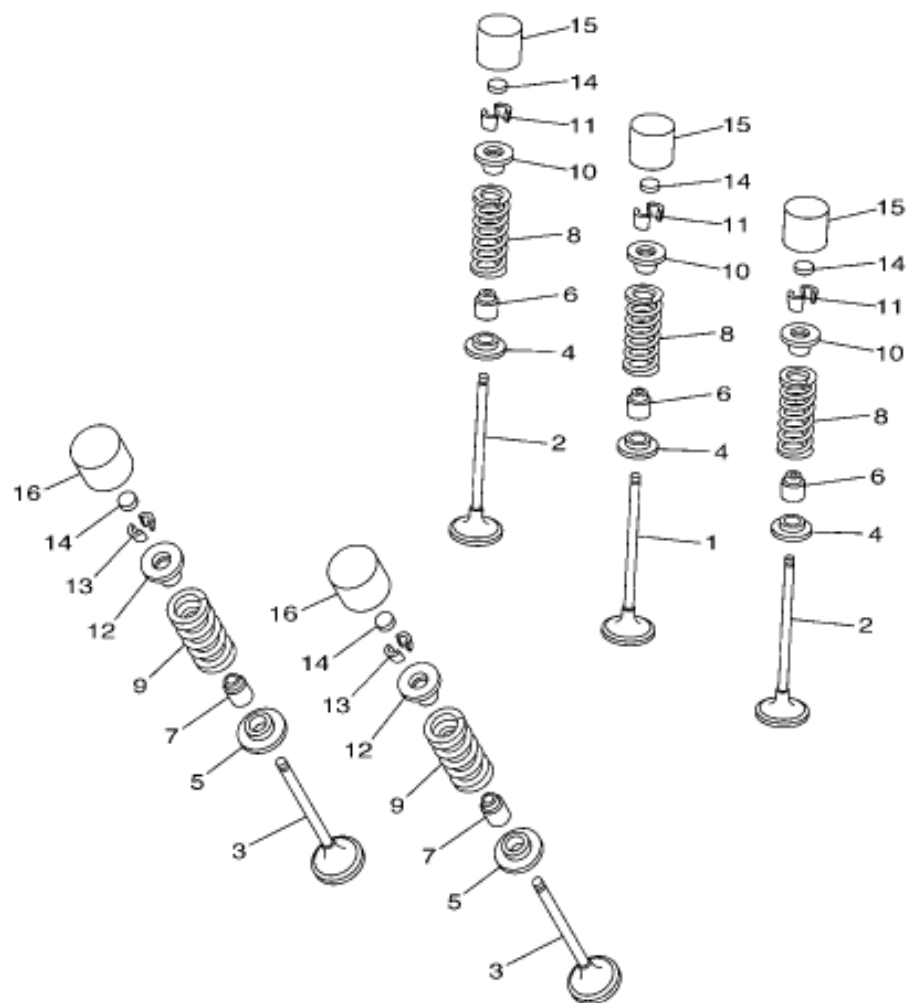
SOUPAPES / VALVE / VÁLVULAS
